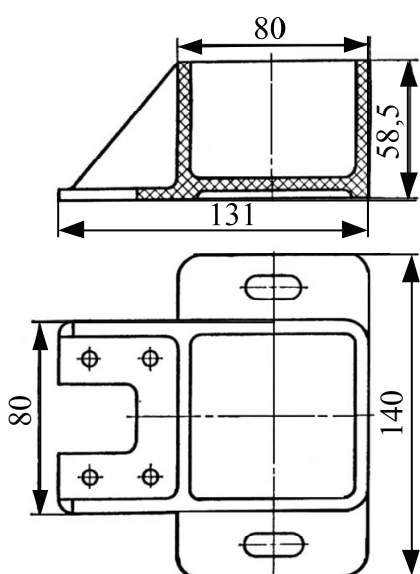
Ребра жесткости на корпусе смазывающего устройства
